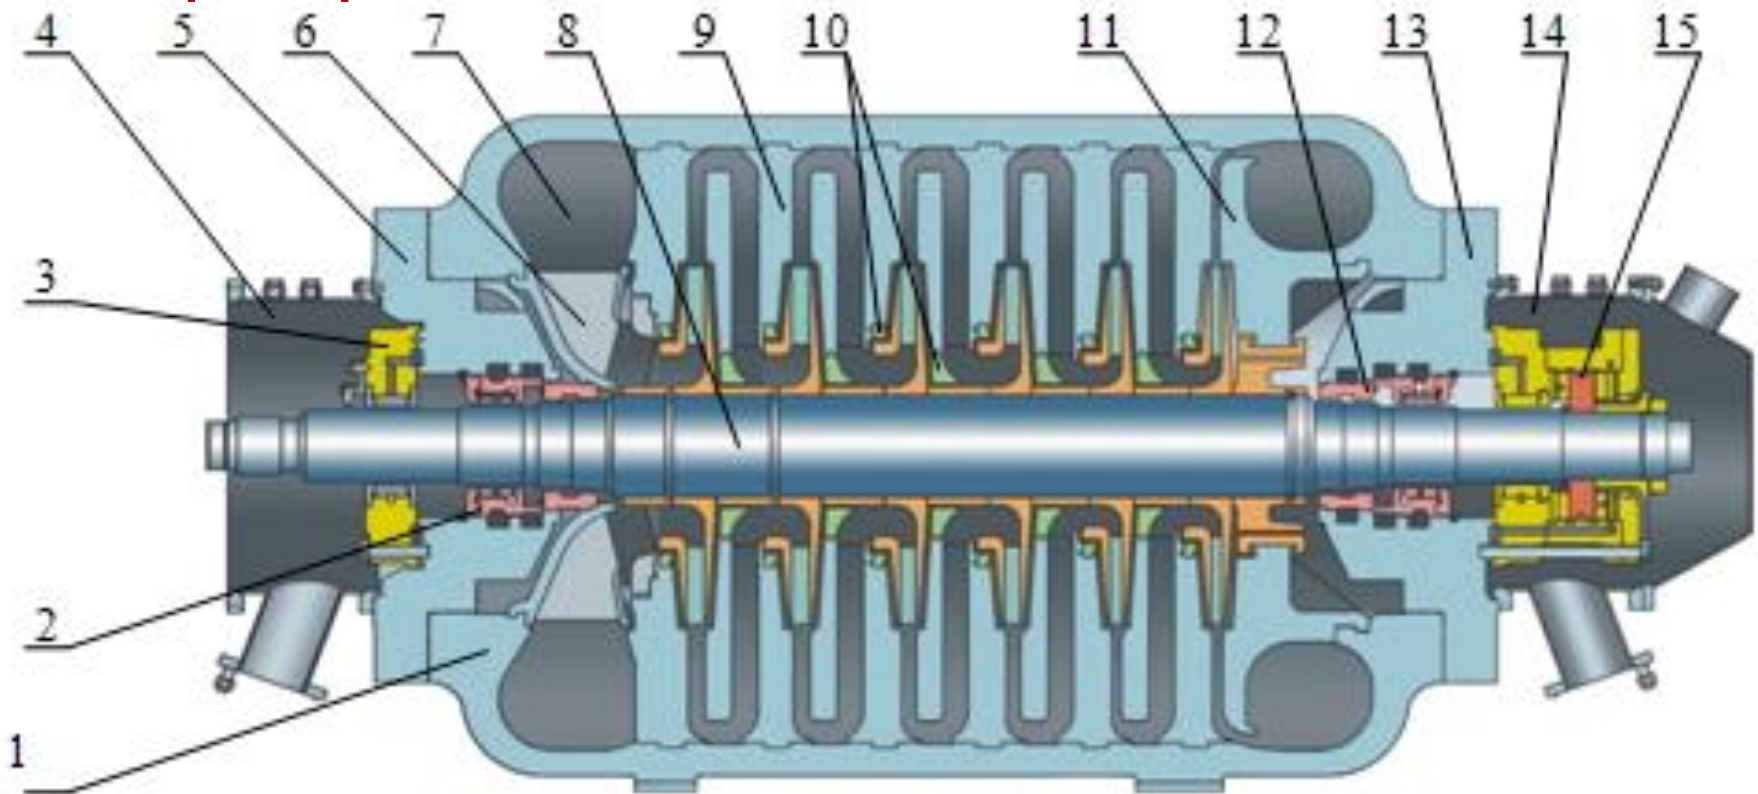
Центробежный компрессор с горизонтальным разъемом корпуса:
